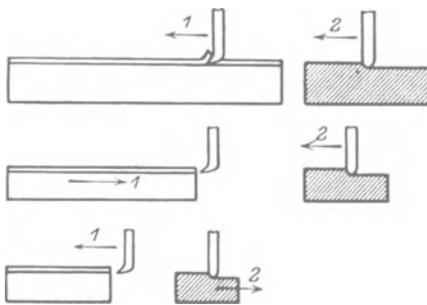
bis 381. Arbeitsweise der Hobelmaschinen.
